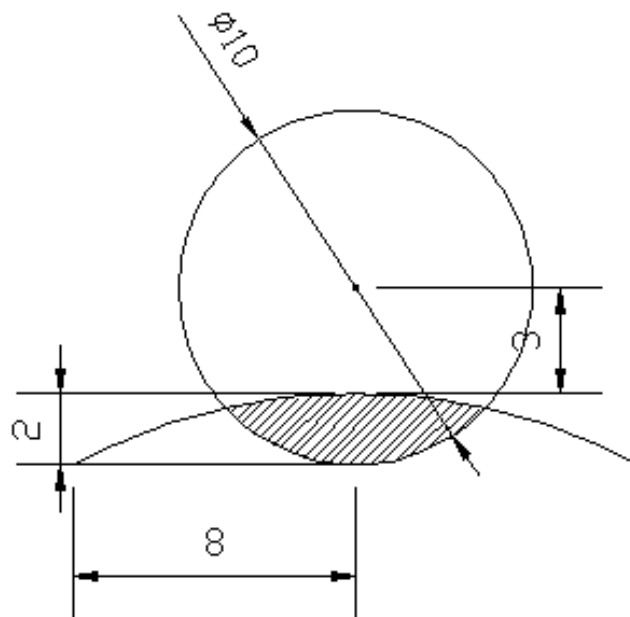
Vista transversal de la secci3n fisurada para la barra 12
